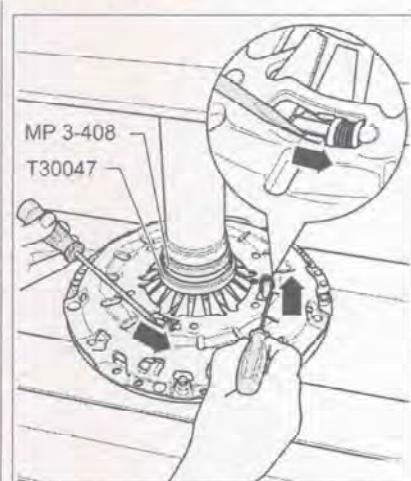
Двумя отвертками равномерно поворачивайте регулировочное кольцо в направлении стрелок до упора.
